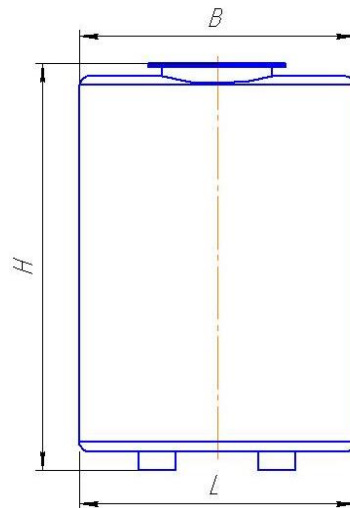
Вертикальный резервуар, однокамерный с плоскими днищами.
